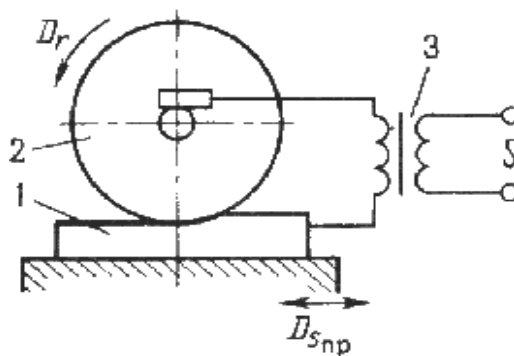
Схема електроконтактної обробки плоскої поверхні:
